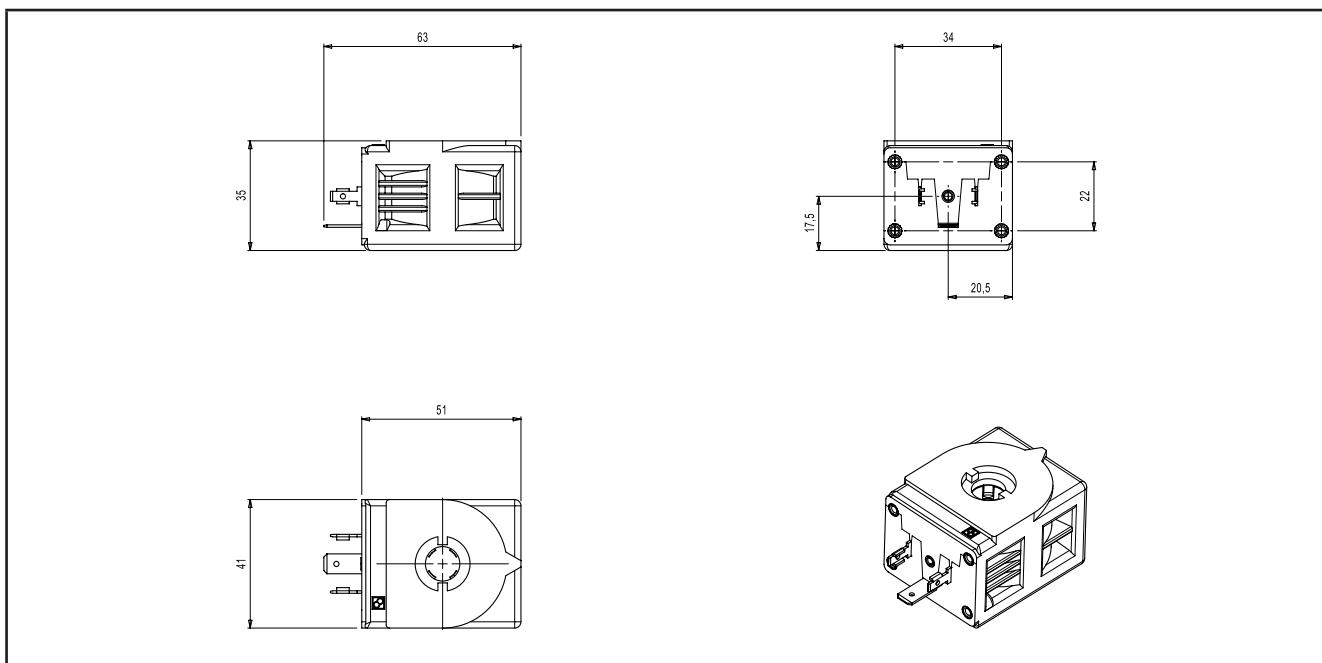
dimensões mecânicas da bobina modelos PXVB0ARA60100, PXVB0ARA20100
